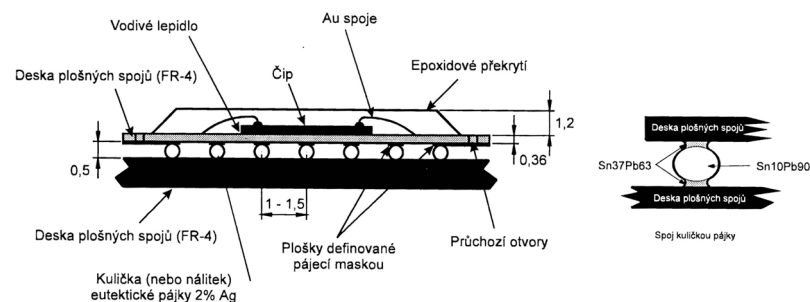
Rozmístění kontaktů u pouzder BGA.
